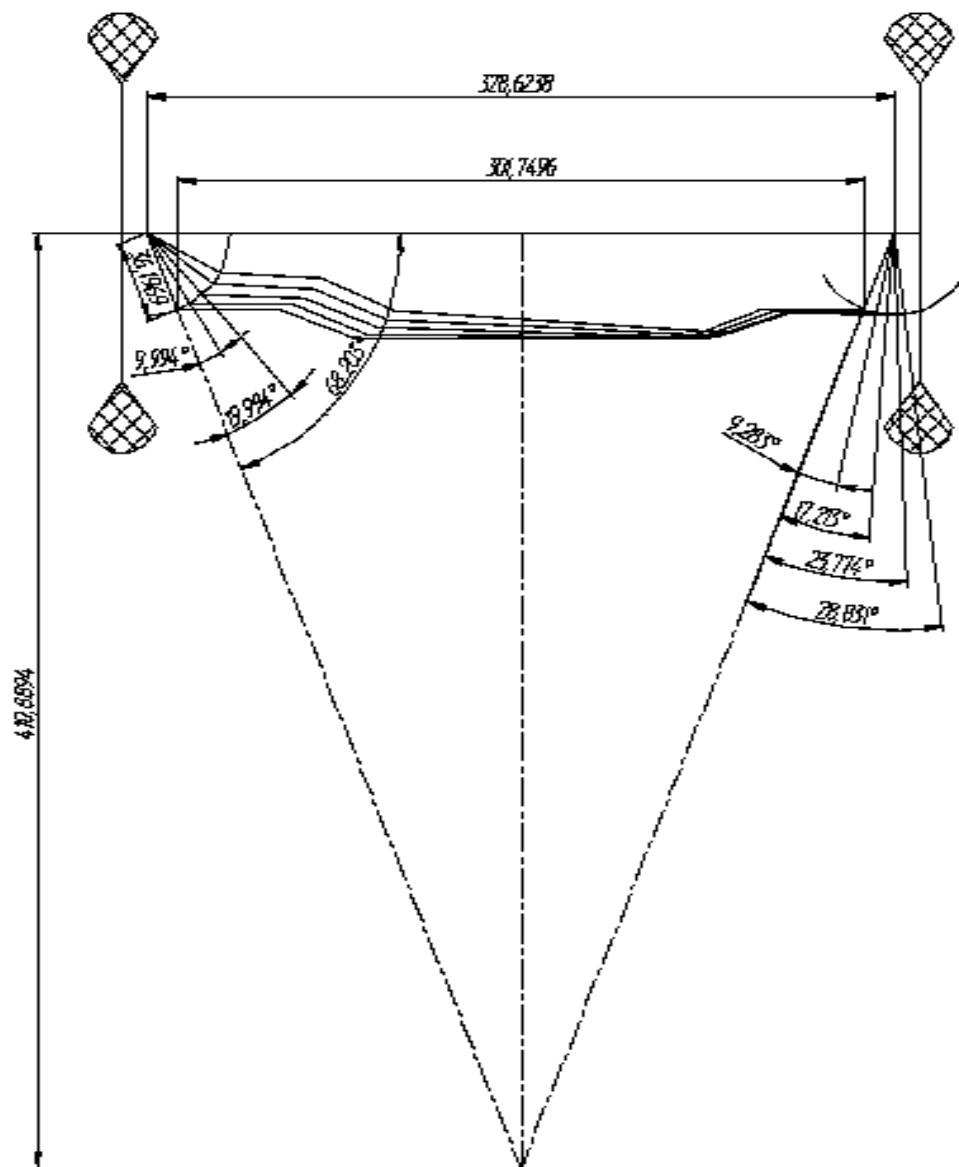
Схема кінематичного роз'язування кермової тяги
